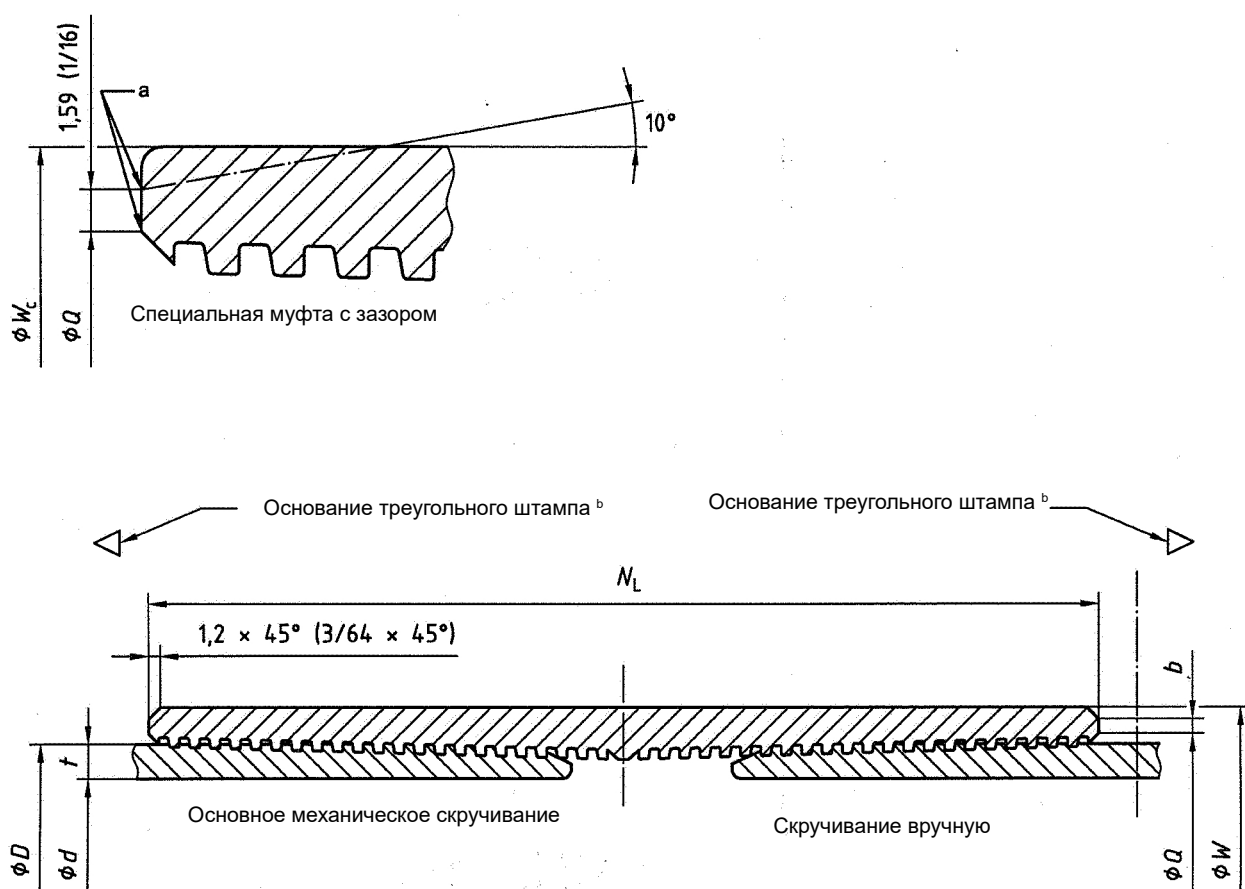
Обсадные трубы и муфты с короткой закругленной резьбой
